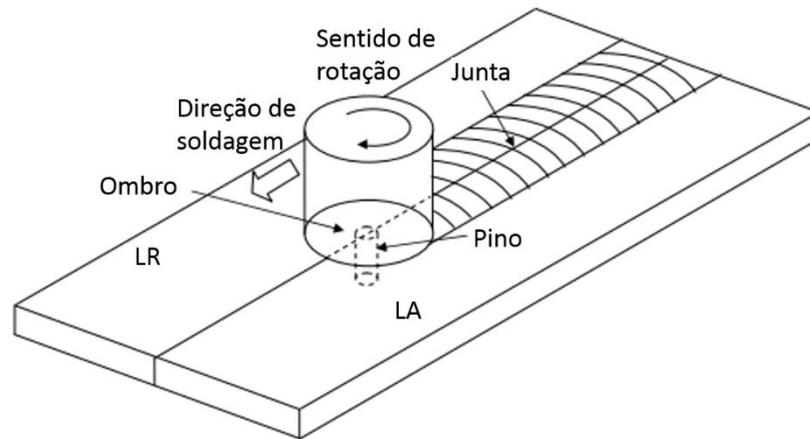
Esquema dos componentes do processo de *friction stir welding*. LR = Lado de retrocesso, LA= Lado de avanço. Adaptado de (NANDAN; DEBROY; BHADESHIA, 2008).
